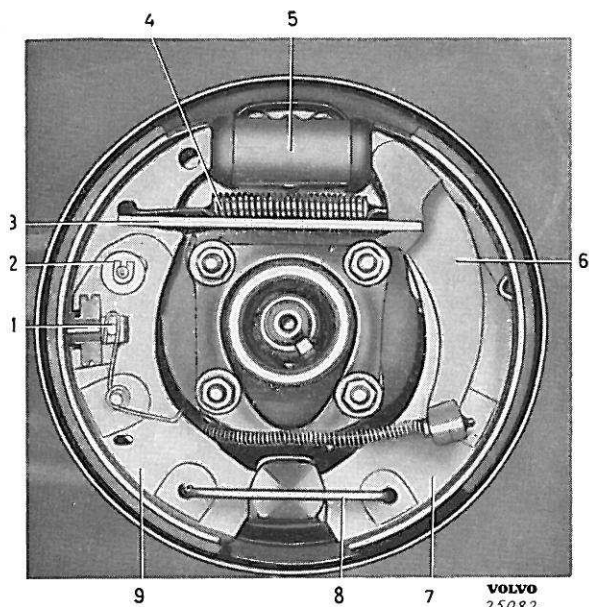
Frein de roue d'ancien modèle, roue arrière gauche.
